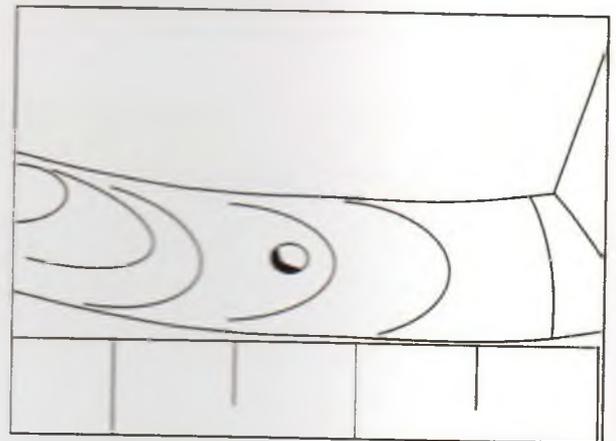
Пора в угловом сварном соединении штуцера с трубопроводом
